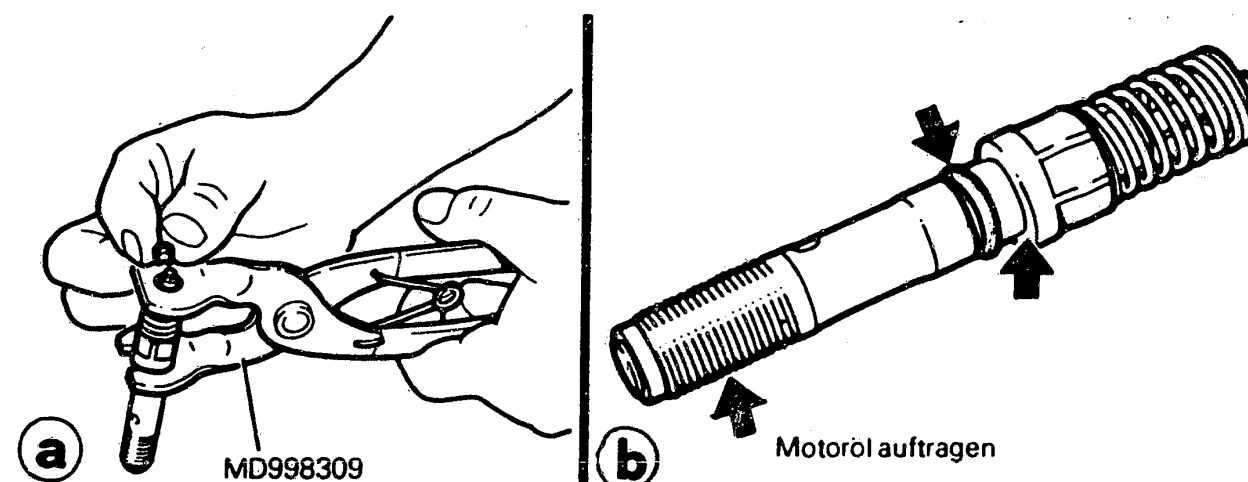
a) Zusammenbau des Jetventils mit Ventilfederzange. b) Beim Einbau des Ventils ist ein neuer O-Ring zu verwenden. An den mit Pfeilen bezeichneten Stellen ist Motorenöl aufzutragen.
